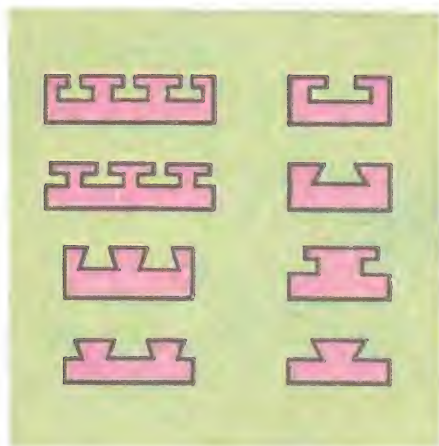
Пластины с различными крепежными выступами для коллекторов на пластмассе
